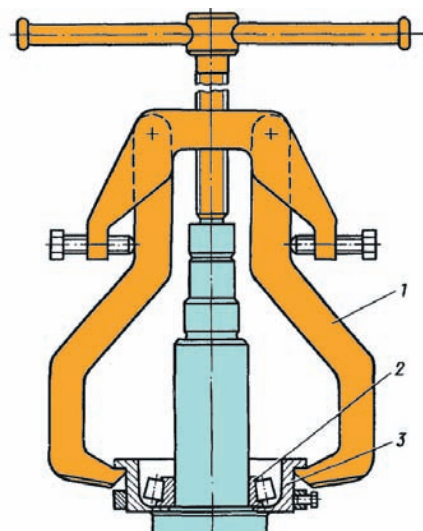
Снятие внутреннего кольца наружного подшипника цилиндрической шестерни среднего моста: 1 — съемник; 2 — внутреннее кольцо подшипника; 3 — оправка в сборе
